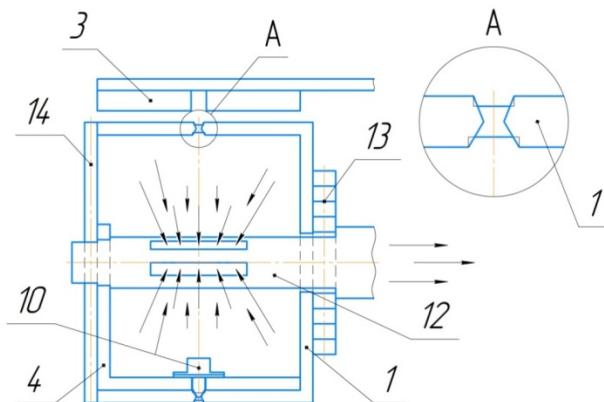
Схема высевающего барабана пневматического высевающего аппарата сеялки точного высева (вид спереди)
